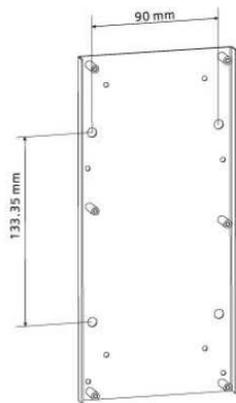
Tamanho de instalação para montagem em gabinete
